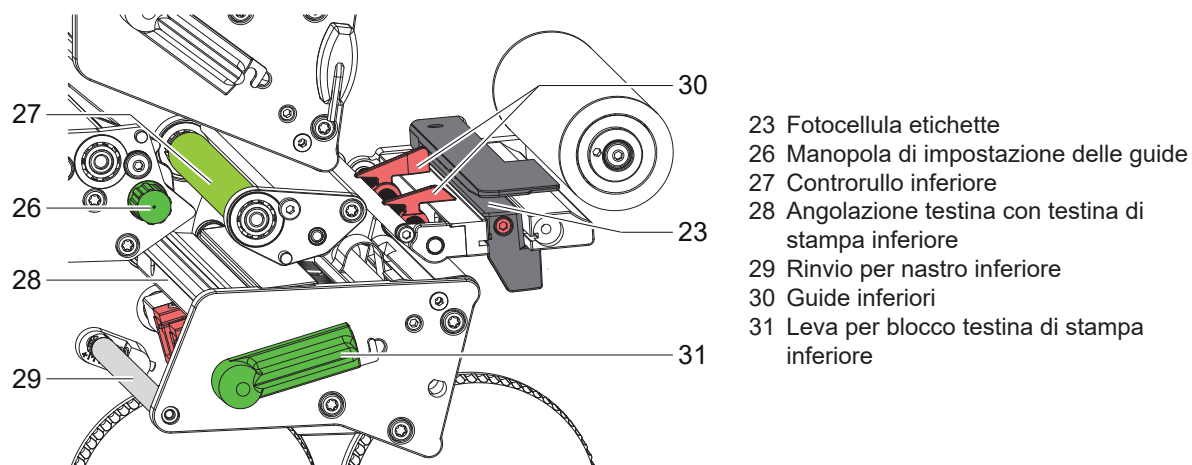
Meccanica di stampa - Gruppo di stampa inferiore
